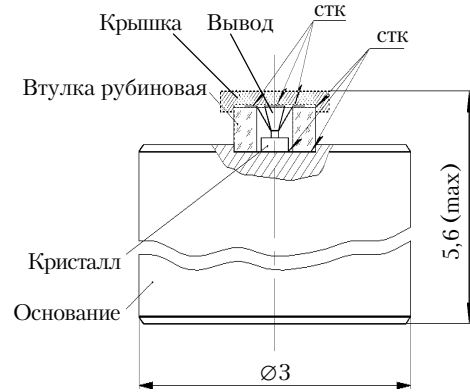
Конструкция кремниевого IMPATT-диода миллиметрового диапазона: стк — сварка термокомпрессионная
